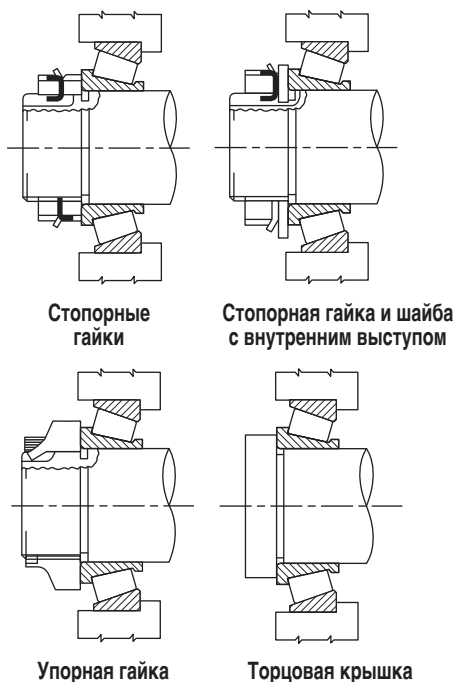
Приспособления для регулировки подшипника (схема монтажа «Х»).
